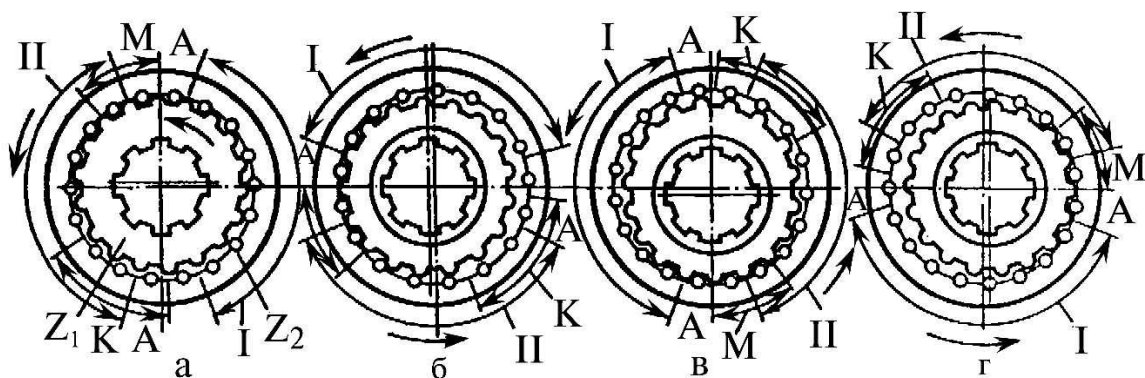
Схема руху ротора і гідравлічного поля планетарної ГМ
